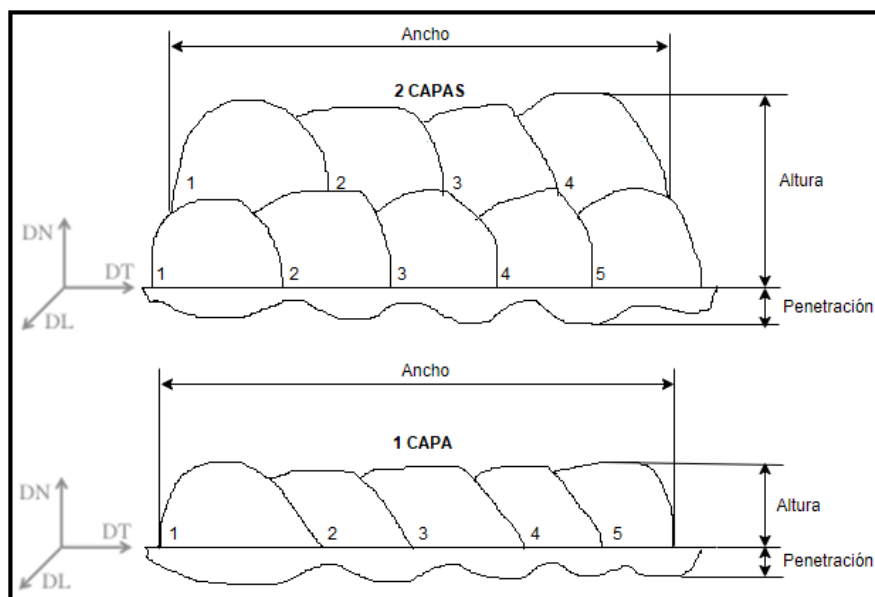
Características geométricas de los recubrimientos de soldaduras LDSS.
